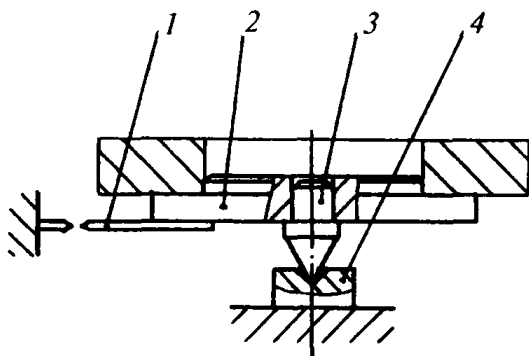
Схема устройства для статической балансировки деталей на призмах:
